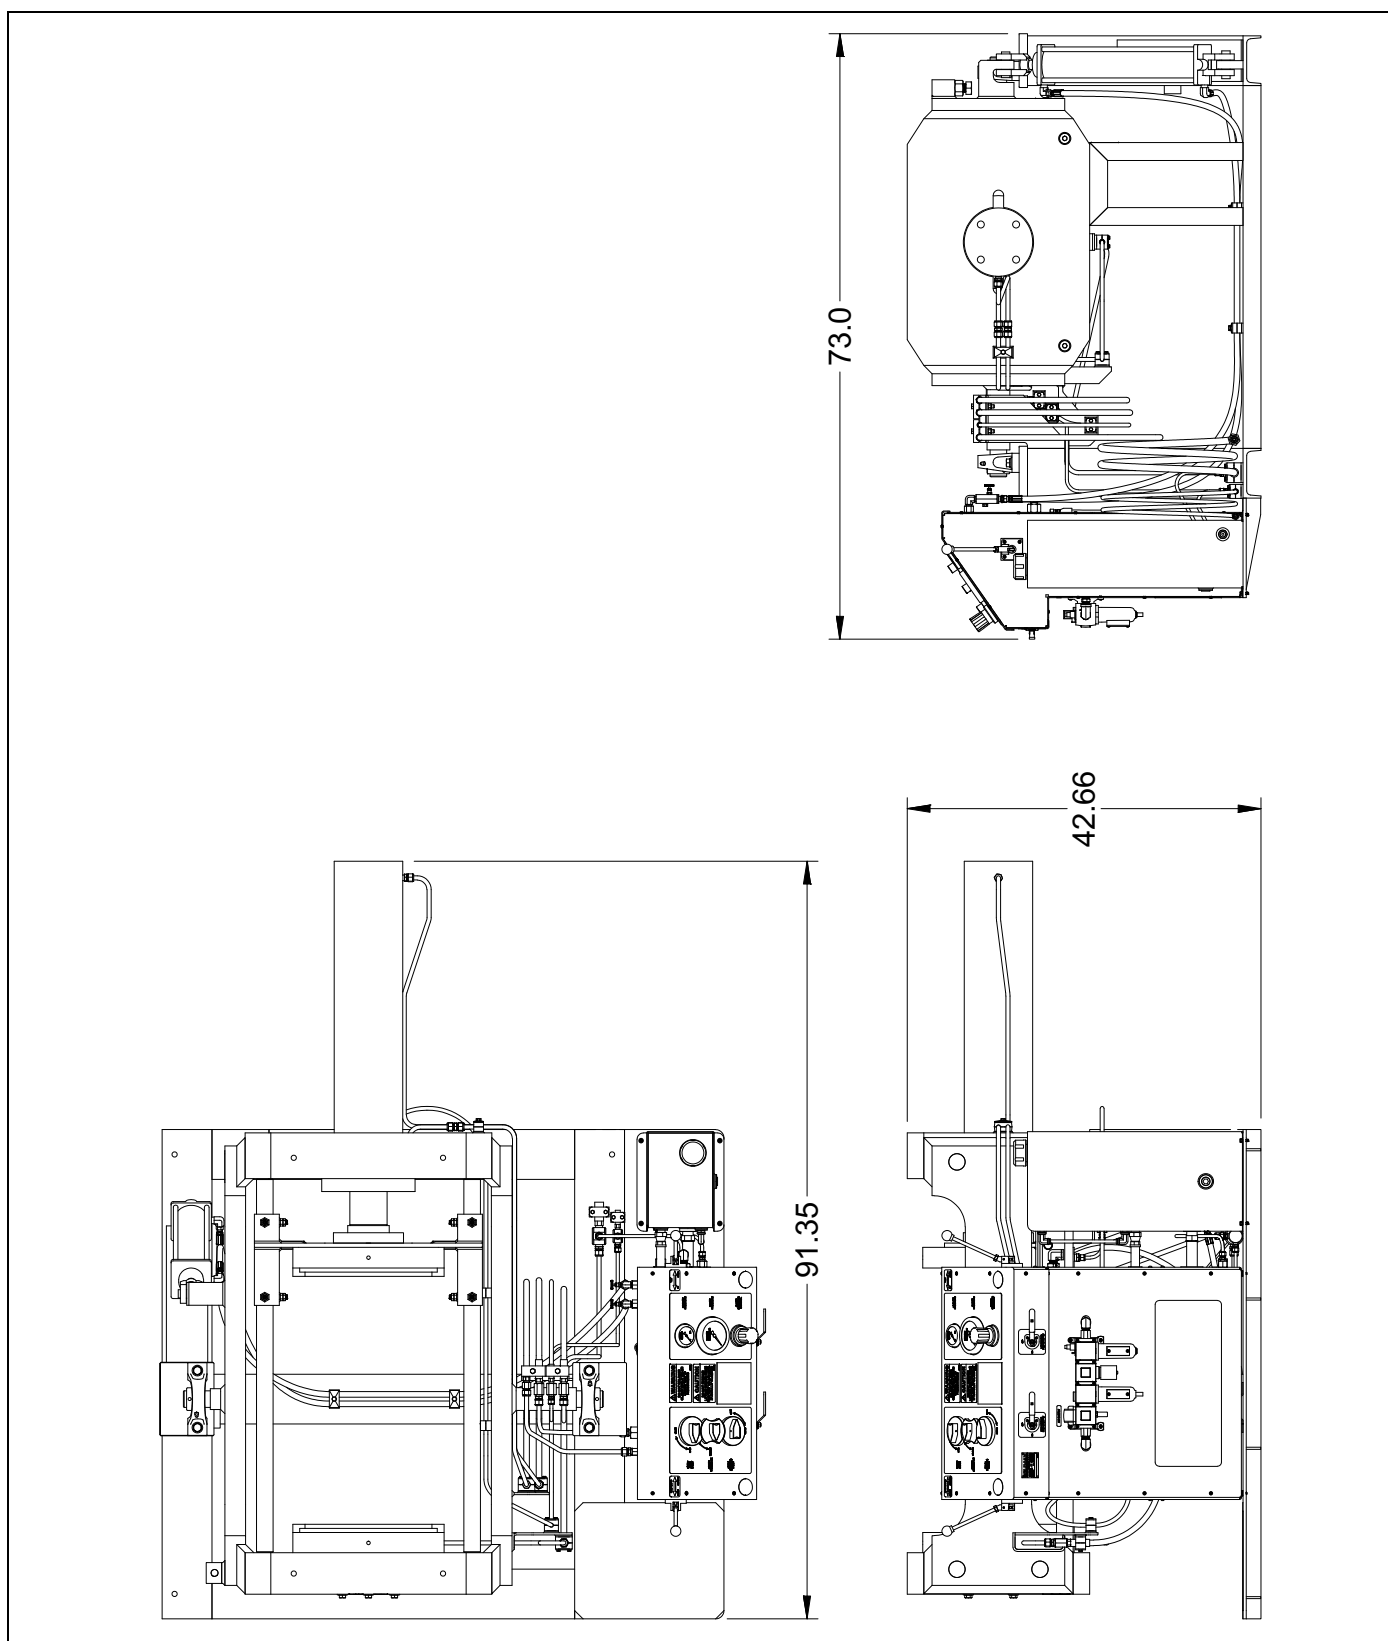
DIMENSIONS DU SYSTÈME DE SERRAGE
